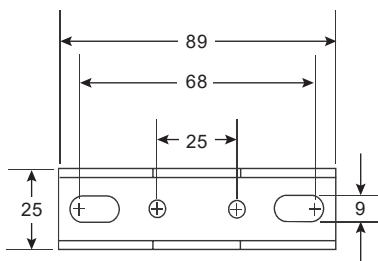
Kit de montaje en carril DIN (incluido con la unidad)
